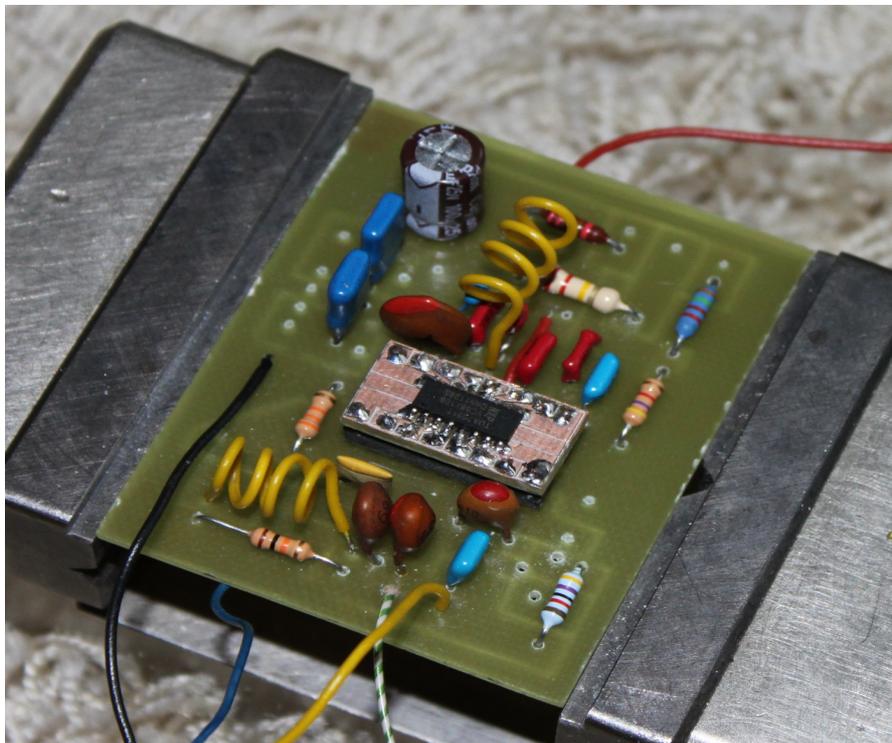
Der erste Testaufbau des HF-Teils auf einer gefrästen Platine
